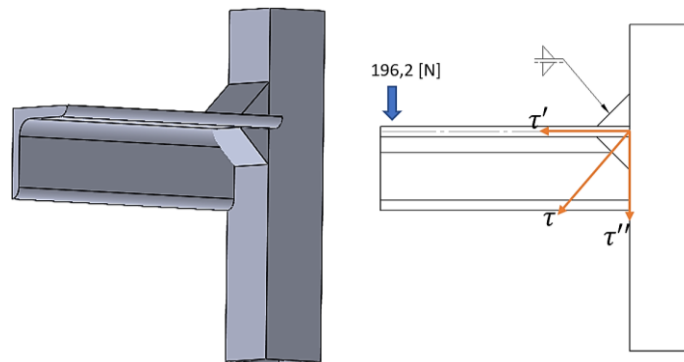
Soldadura sometida a flexión del perfil tipo L.
